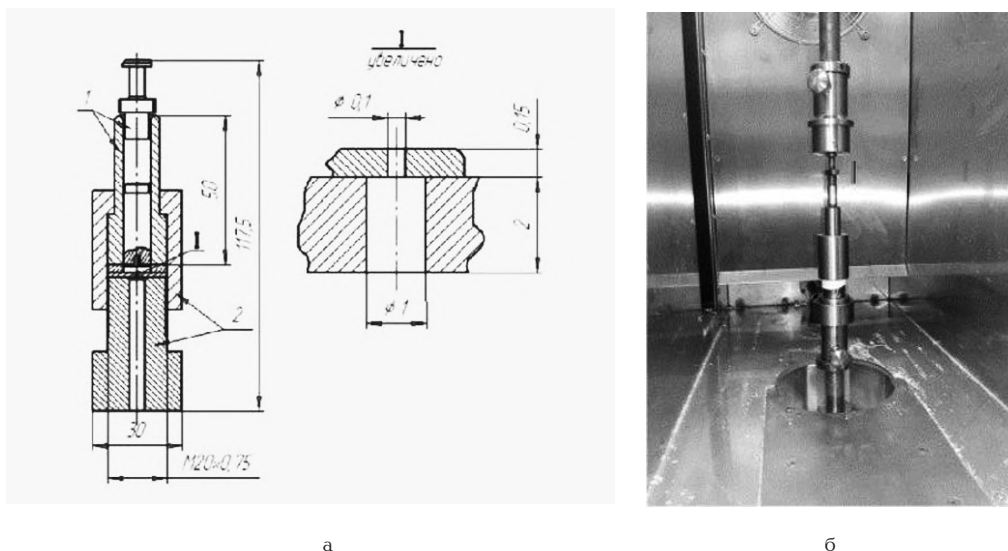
Фильерный узел: 1 — плунжерная пара, 2 — корпус;
